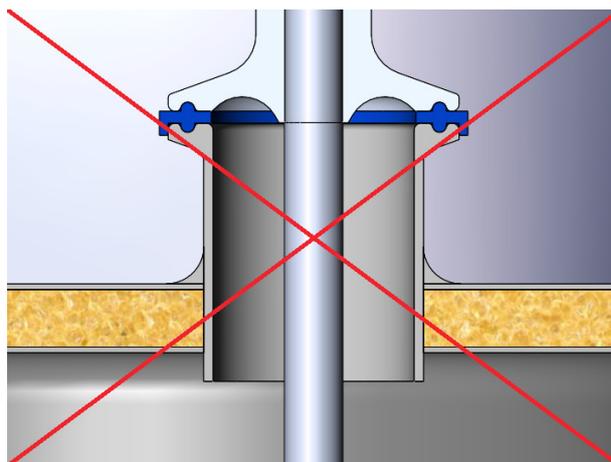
No soldado a ras en el interior y pulido
